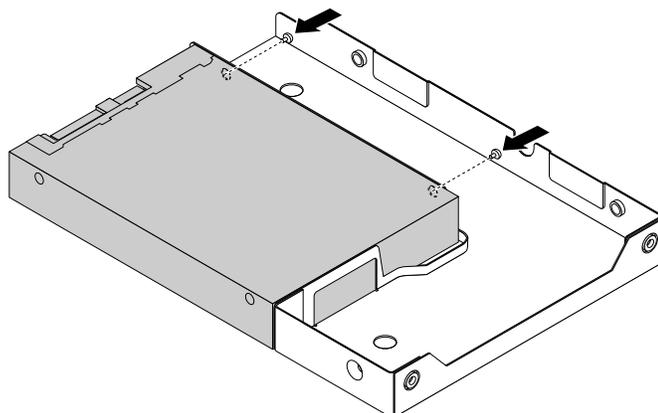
Serrage des vis pour fixer l'unité 2,5 pouces sur l'adaptateur de disque
